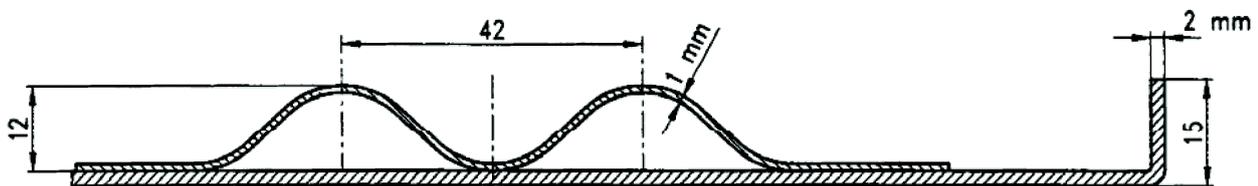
Querschnitt durch die wassergekühlte Stahlplatte
